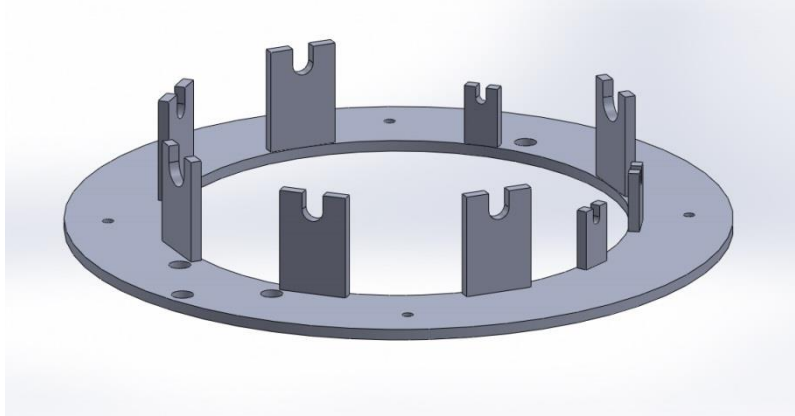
Vista dimétrica del ensamblaje de soportes.
